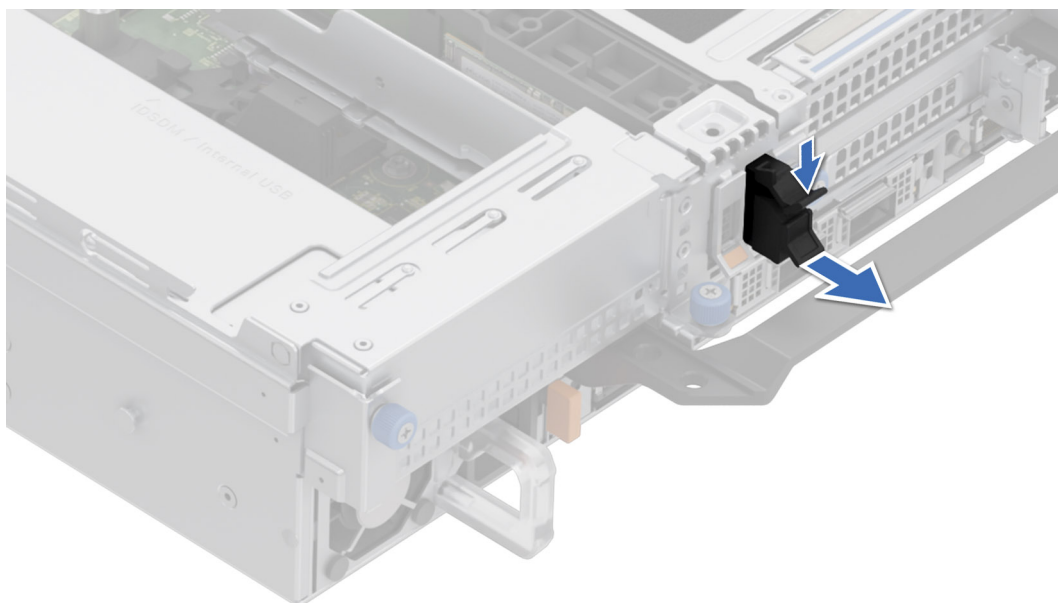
Retrait de la plaque de recouvrement de la carte BOSS
